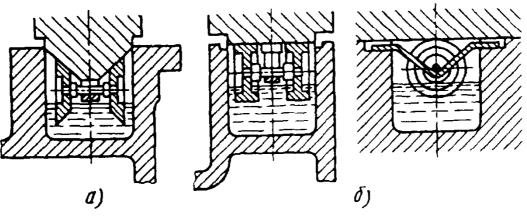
Роликовая смазка направляющих: a - призматических; δ - плоских
